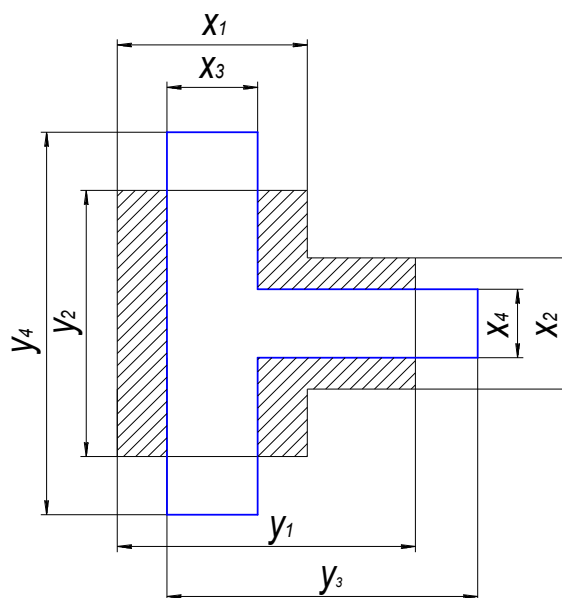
Схема деформации металла при прокатке тавровой заготовки в трехвалковом калибре
